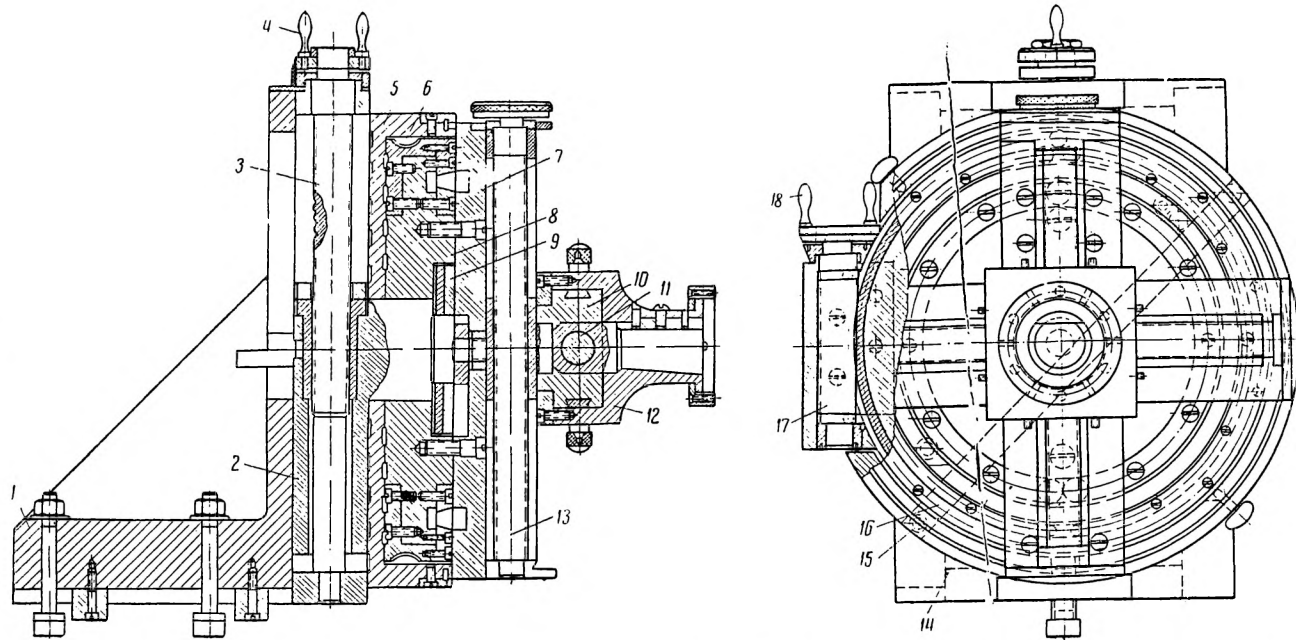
Приспособление конструкции Андрианова для координатного метода шлифования шаблонов и лекал
